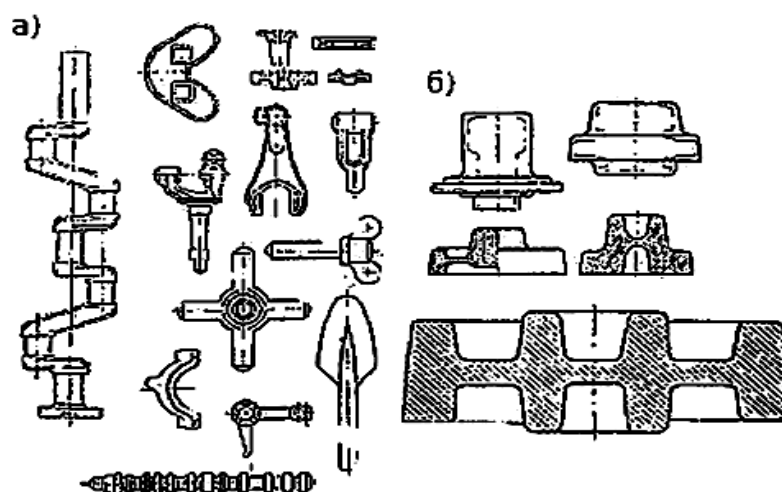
Типовые штамповки изготовленные в открытых штампах (а) и закрытых штампах (б)
